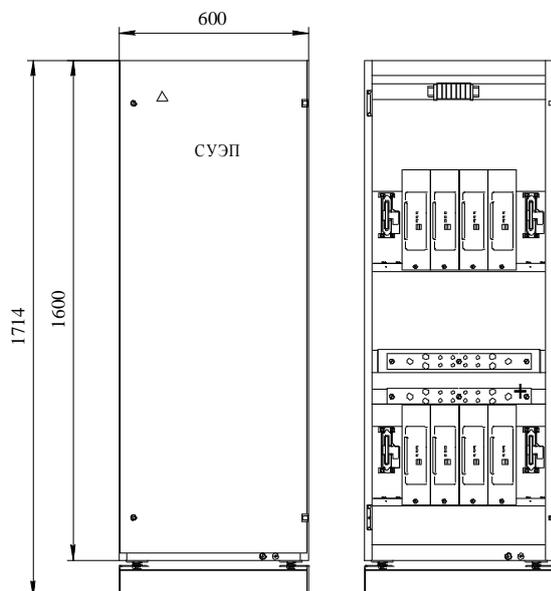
Габаритный чертеж СУЭП-3-В (глубина стойки 600мм)
